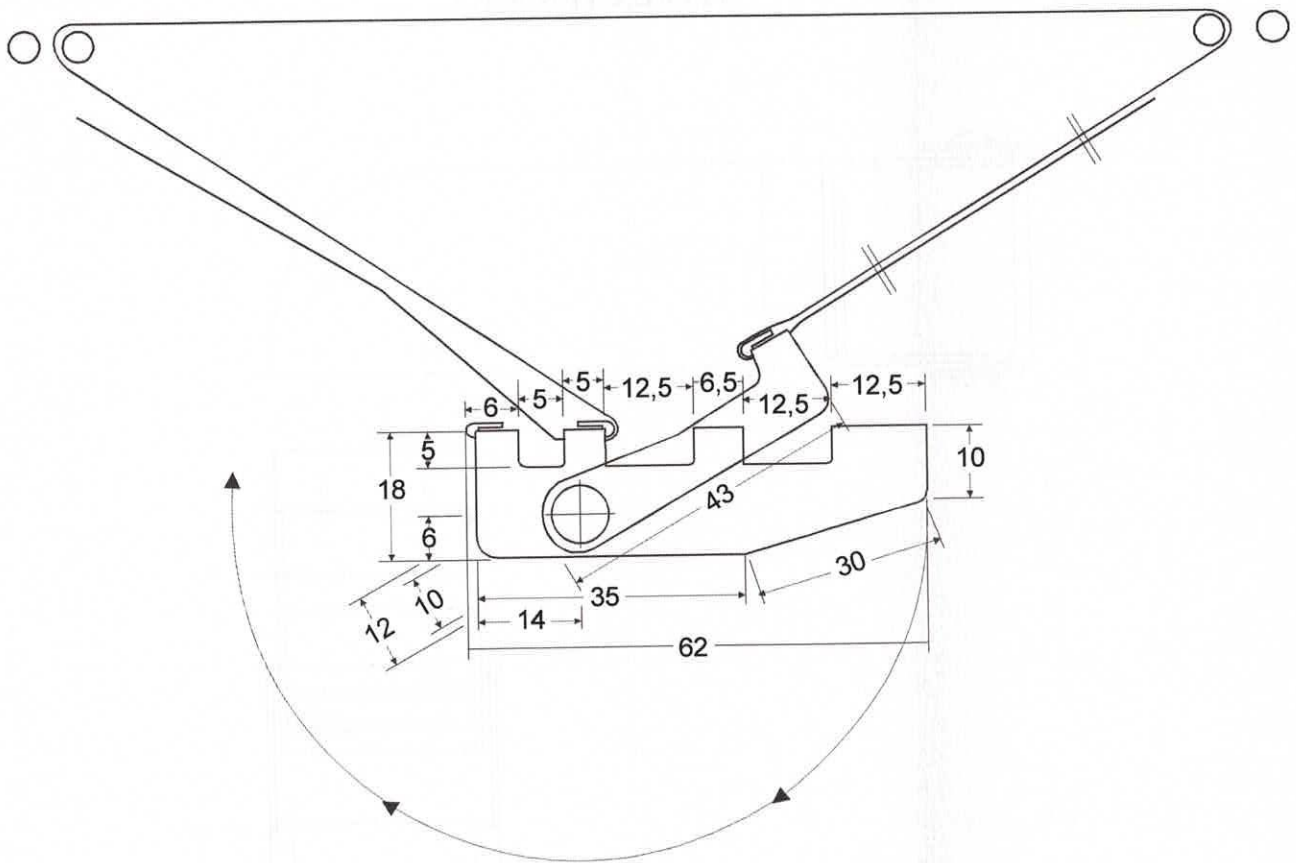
Vista da fivela tensora aberta (medidas em mm)
